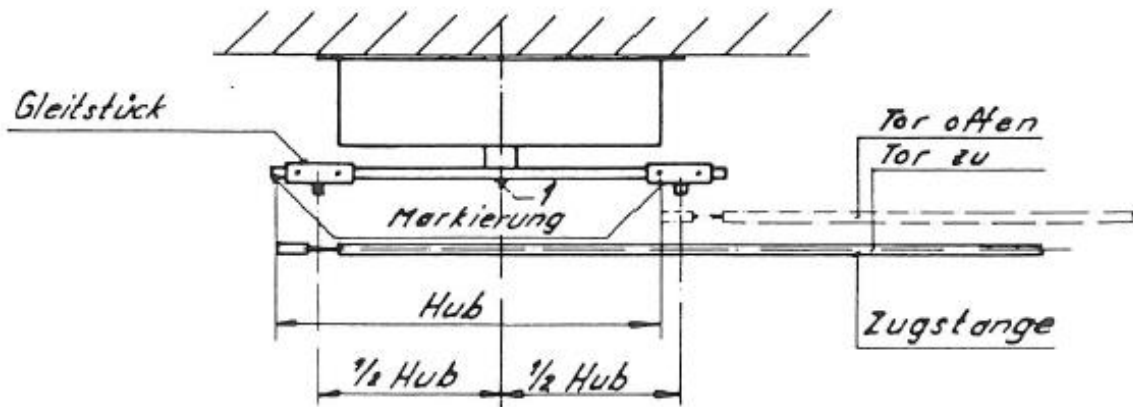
Vorderansicht Drehteller mit Zugstange
